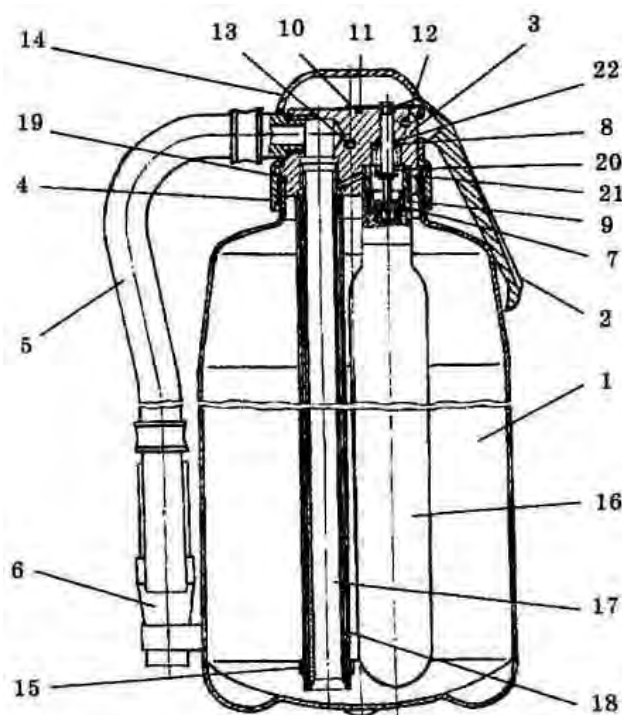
Вогнегасник порошковий ВП-5 : 1– корпус; 2 – ручка; 3 – головка; 4 – гайка накидна; 5 – рукав; 6 – пістолет-розпилювач; 7 – голка; 8 – шайба; 9 – перехідник; 10 – підхват голки; 11 – запобіжна чека; 12 – вісь; 13 – штифт; 14 – кільце ущільнювальне; 15 – кільце гумове; 16 – балон з робочим газом; 17 – трубка сифонна; 18-трубка газопідвідна; 19 – кільце ущільнювальне; 20 – пружина; 21 – шайба упорна; 22 – кільце ущільнювальне
